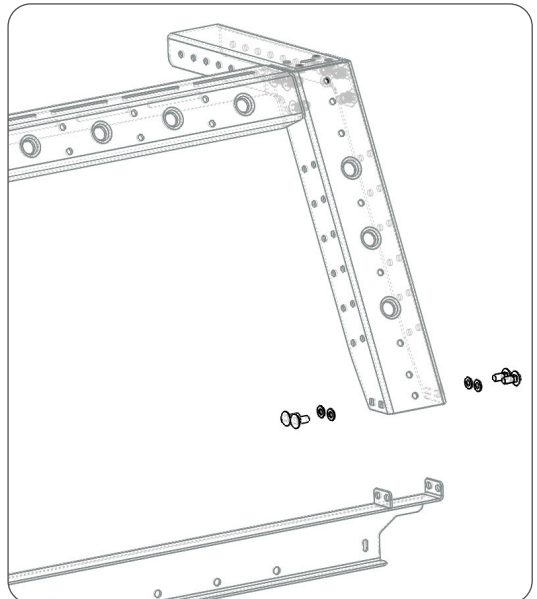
Detailansicht des verschraubten unteren Rahmen / detailed view of bolted down lower frame
